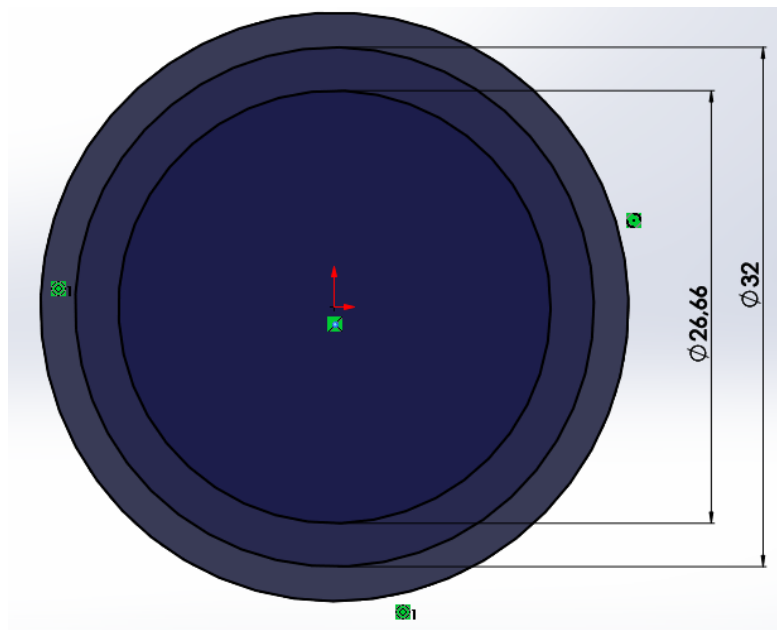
Círculos de diámetro exterior, primitivo e interior del engranaje.
